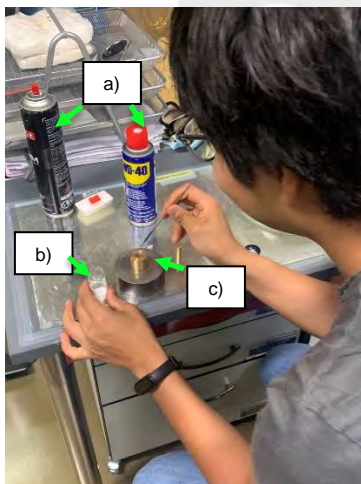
Proceso de agregado del desmoldante (a) y colocación de la muestra (b) en el molde cilíndrico (c).
